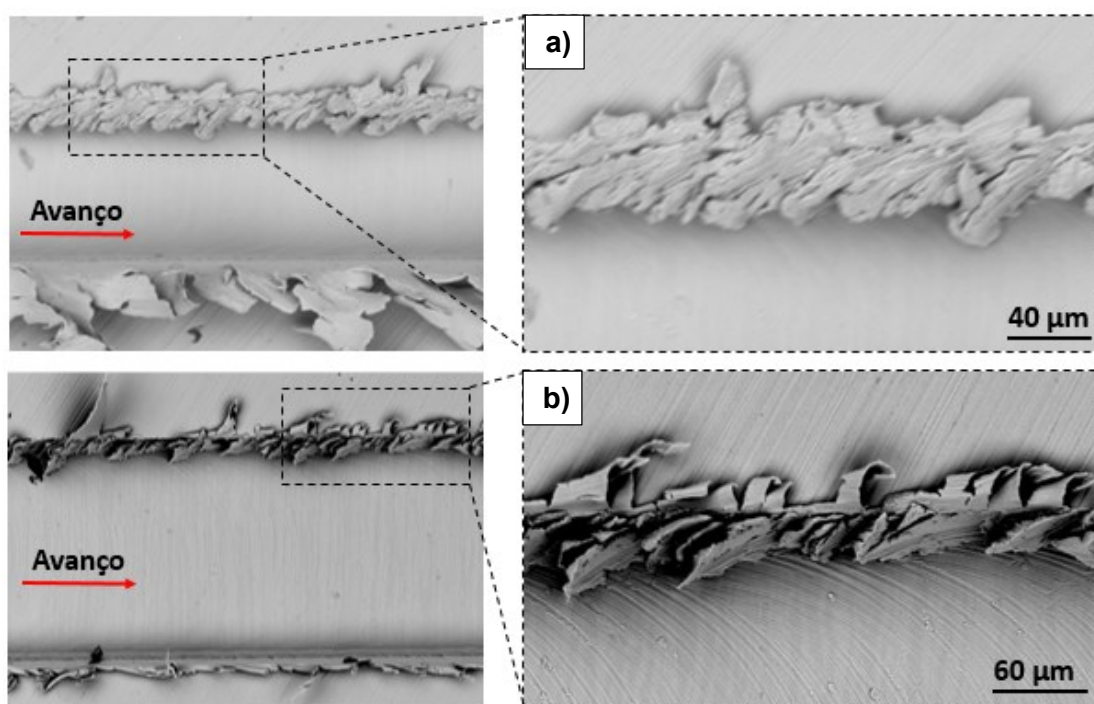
Rebarba interna em (a) ensaios 1 e 2 (b) 2º passe, ensaio 3
